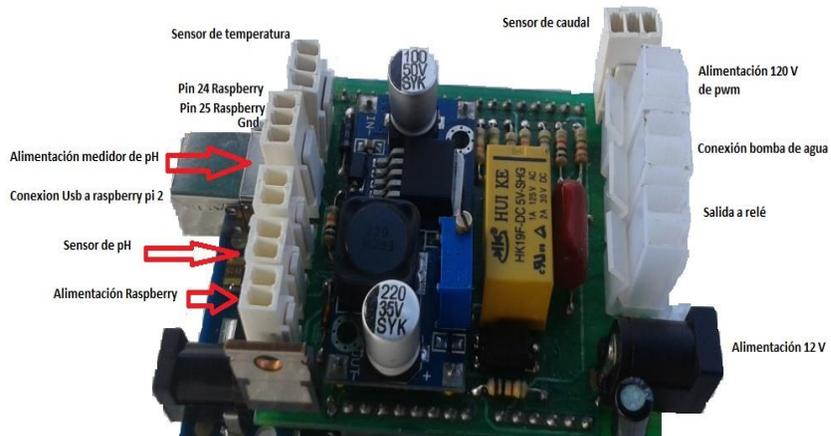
Tarjeta de interfaz implementada para conexión de sensores a) construcción física de la tarjeta. Fuente el autor.
